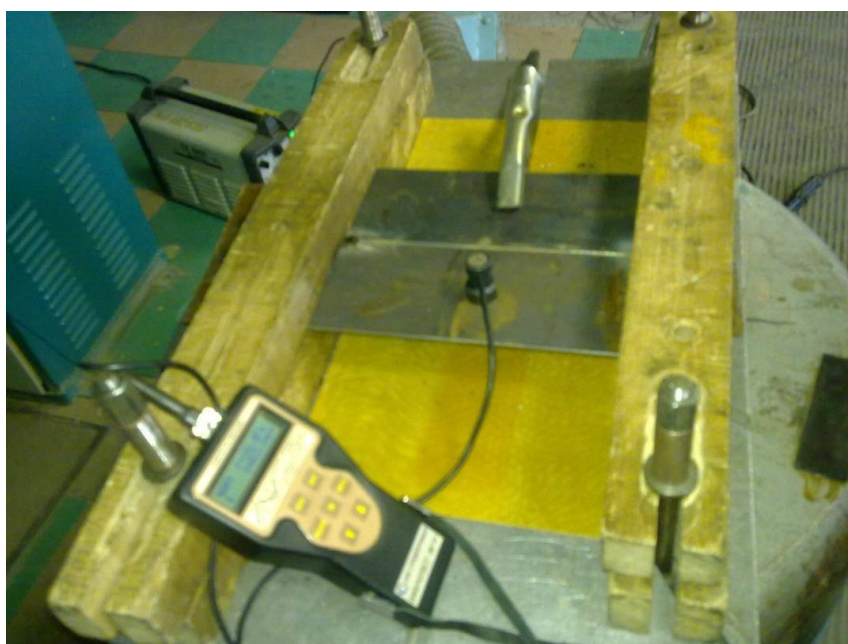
Фото зразка закріпленого на вібростенді ВЕРС-400 перед зварюванням
